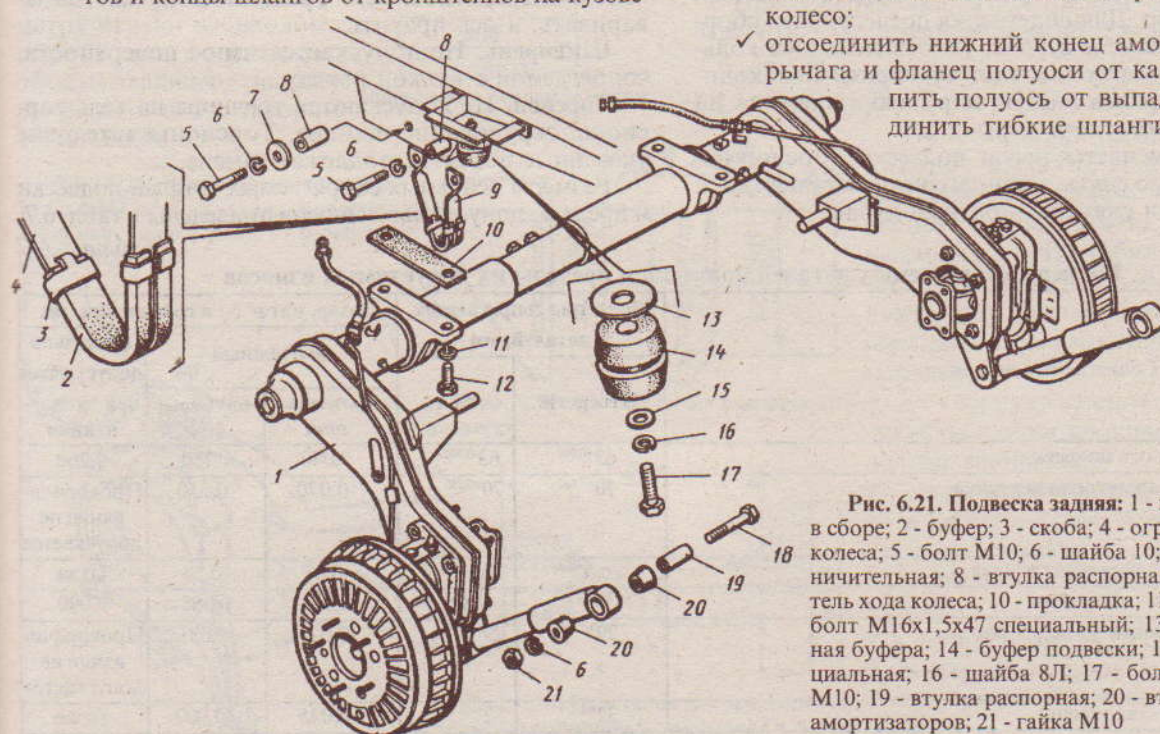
Подвеска задняя: 1 - подвеска задняя в сборе; 2 - буфер; 3 - скоба; 4 - ограничитель хода колеса; 5 - болт М10; 6 - шайба 10; 7 - шайба ограничительная; 8 - втулка распорная; 9 - ограничитель хода колеса; 10 - прокладка; 11 - шайба 16; 12 - болт М16х1,5х47 специальный; 13 - шайба опорная буфера; 14 - буфер подвески; 15 - шайба 8 специальная; 16 - шайба 8Л; 17 - болт М8; 18 - болт М10; 19 - втулка распорная; 20 - втулка шарниров амортизаторов; 21 - гайка М10
